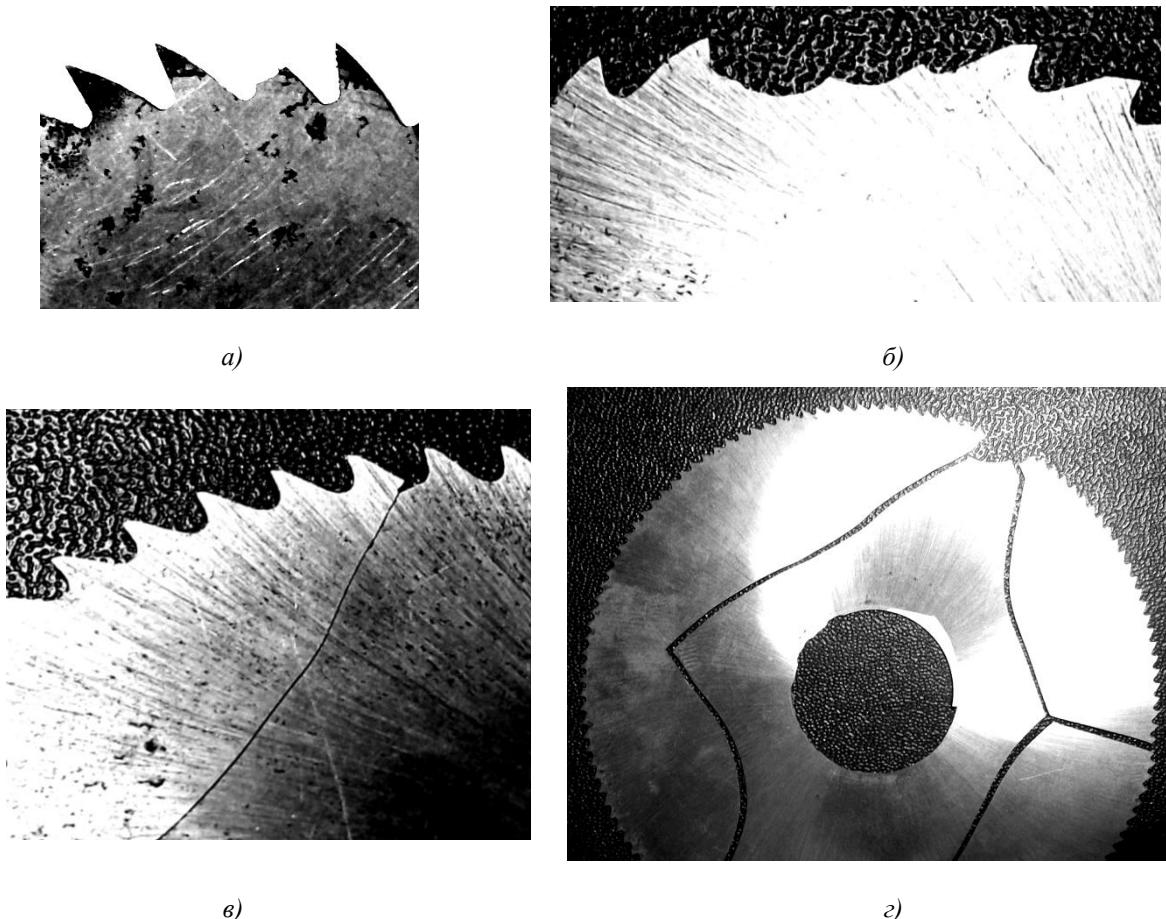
Основні види руйнувань прорізних фрез: а) руйнування вершинної частини зуба; б) обрив зубців по основі; в) утворення тріщин; г) повне руйнування диску фрези
